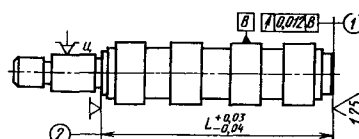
Приспособление для обкатки промежуточных шеек вытяжных цилиндров:
